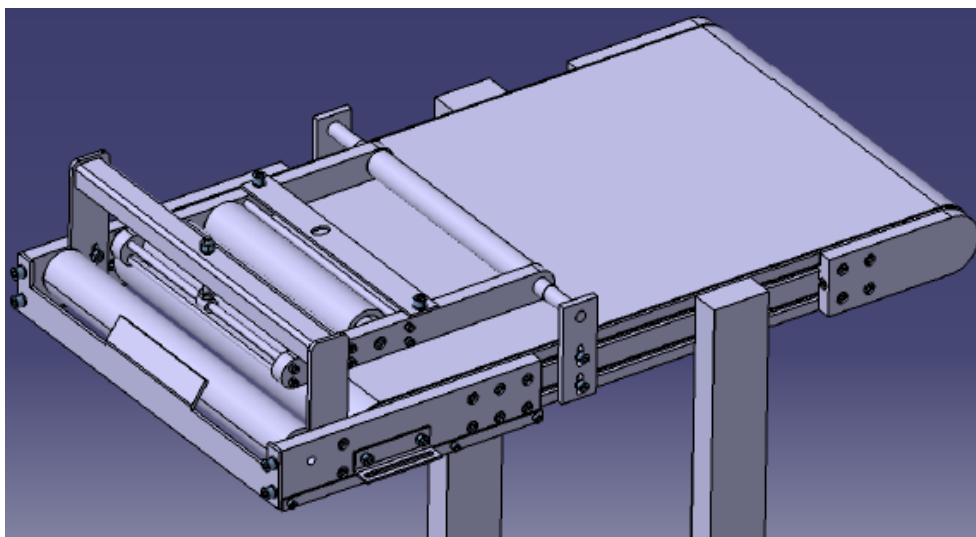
Vizualizace dorazu, přední strana [9]
